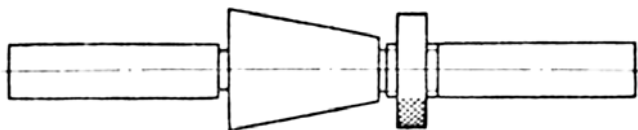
Оправка для балансировки шлифовального круга
